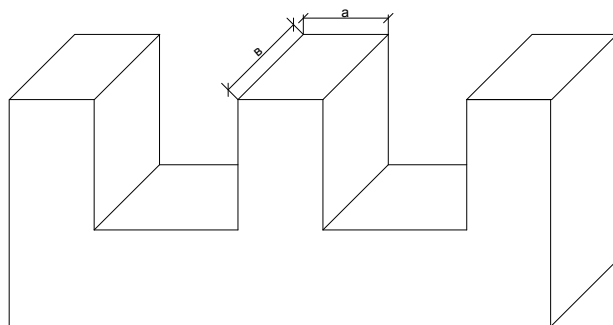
Габаритные размеры сечения магнитопровода магнитного пускателя.
